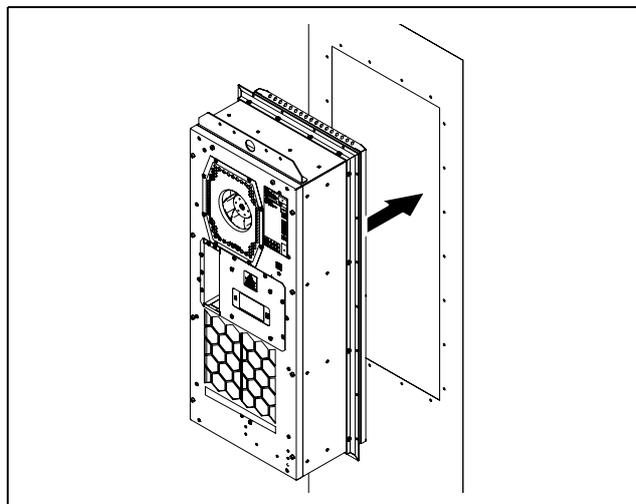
Montaje del refrigerador en una pieza plana de pared simple
